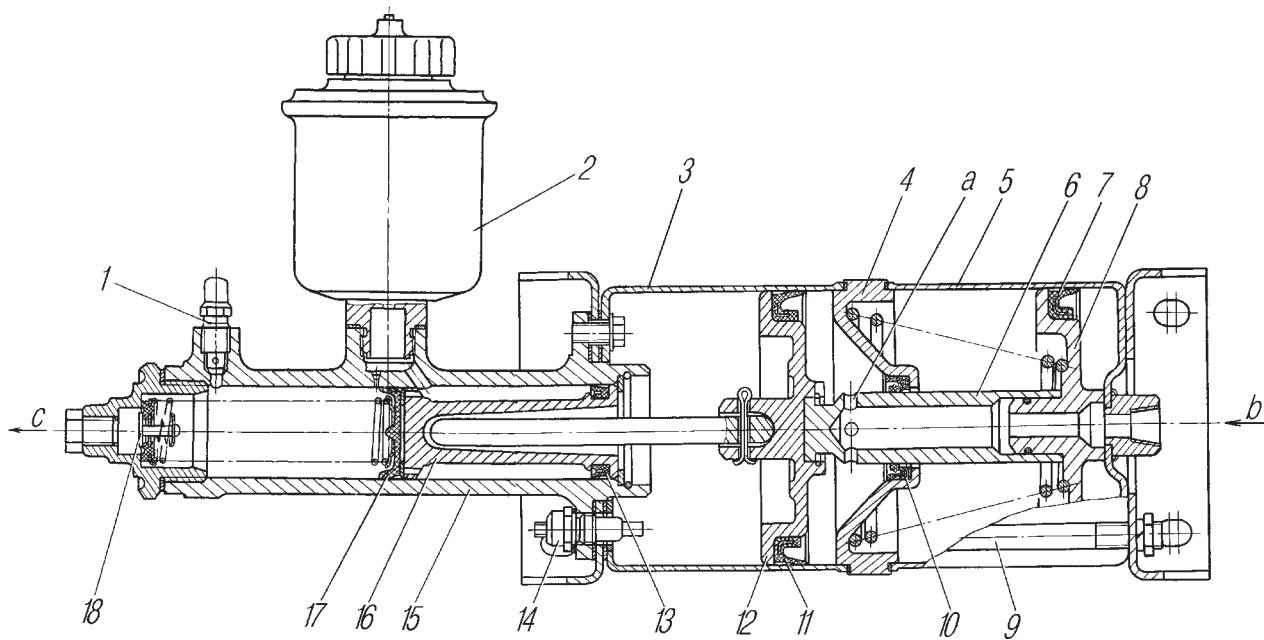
Усилитель пневматический с главным тормозным цилиндром:
